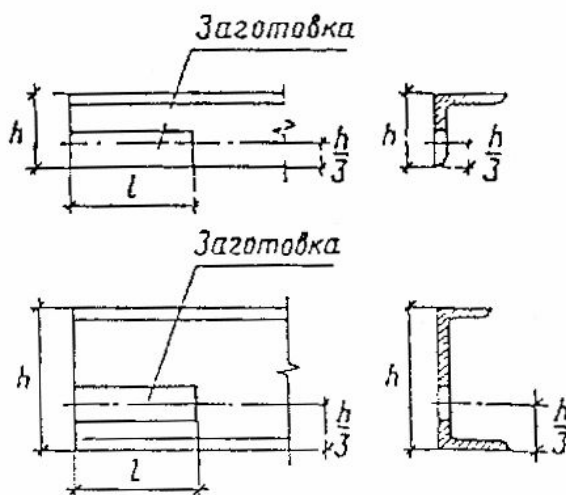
Схема отбора заготовок из уголковых швеллерных сечений
